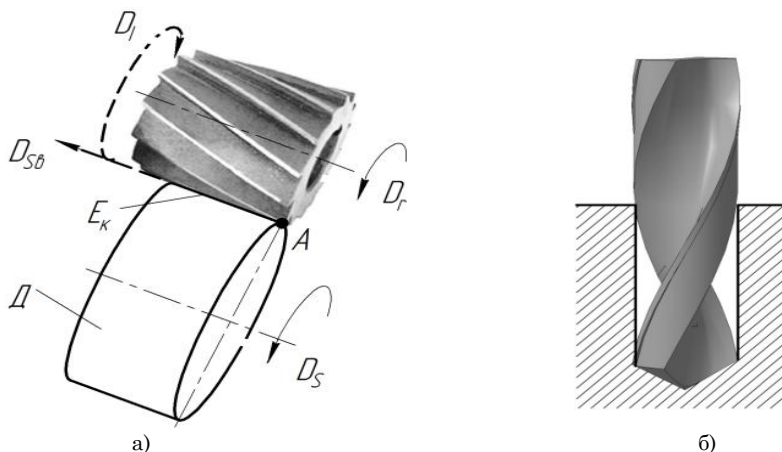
Точковий контакт при створенні тіл обертання: а) циліндричною фрезою; б) спіральним свердлом
